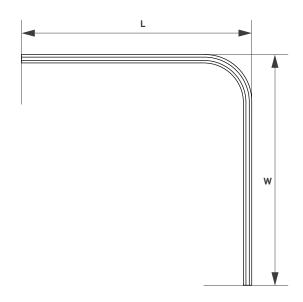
Чертеж и габаритные размеры трека ART-APRIORI-TRACK-ANGLE-A-1722
